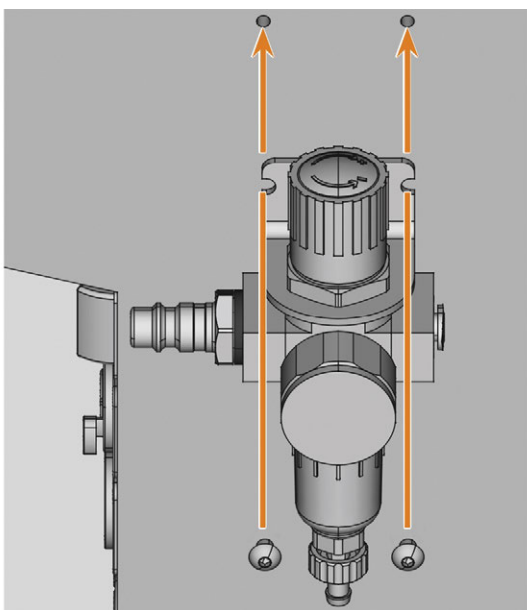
INSTALLIEREN DES DRUCKMINDERERS
